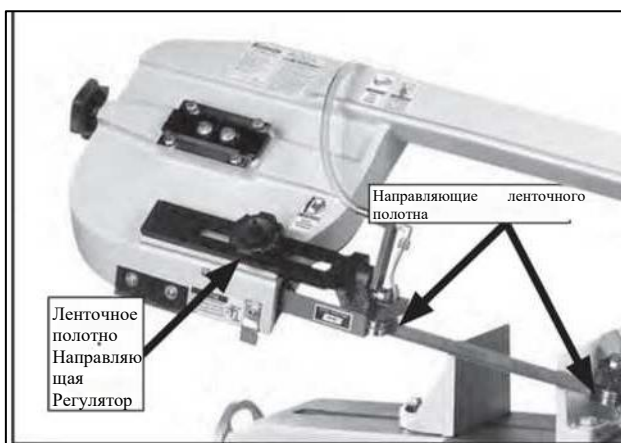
Расположение регулятора направляющей ленточного полотна.
